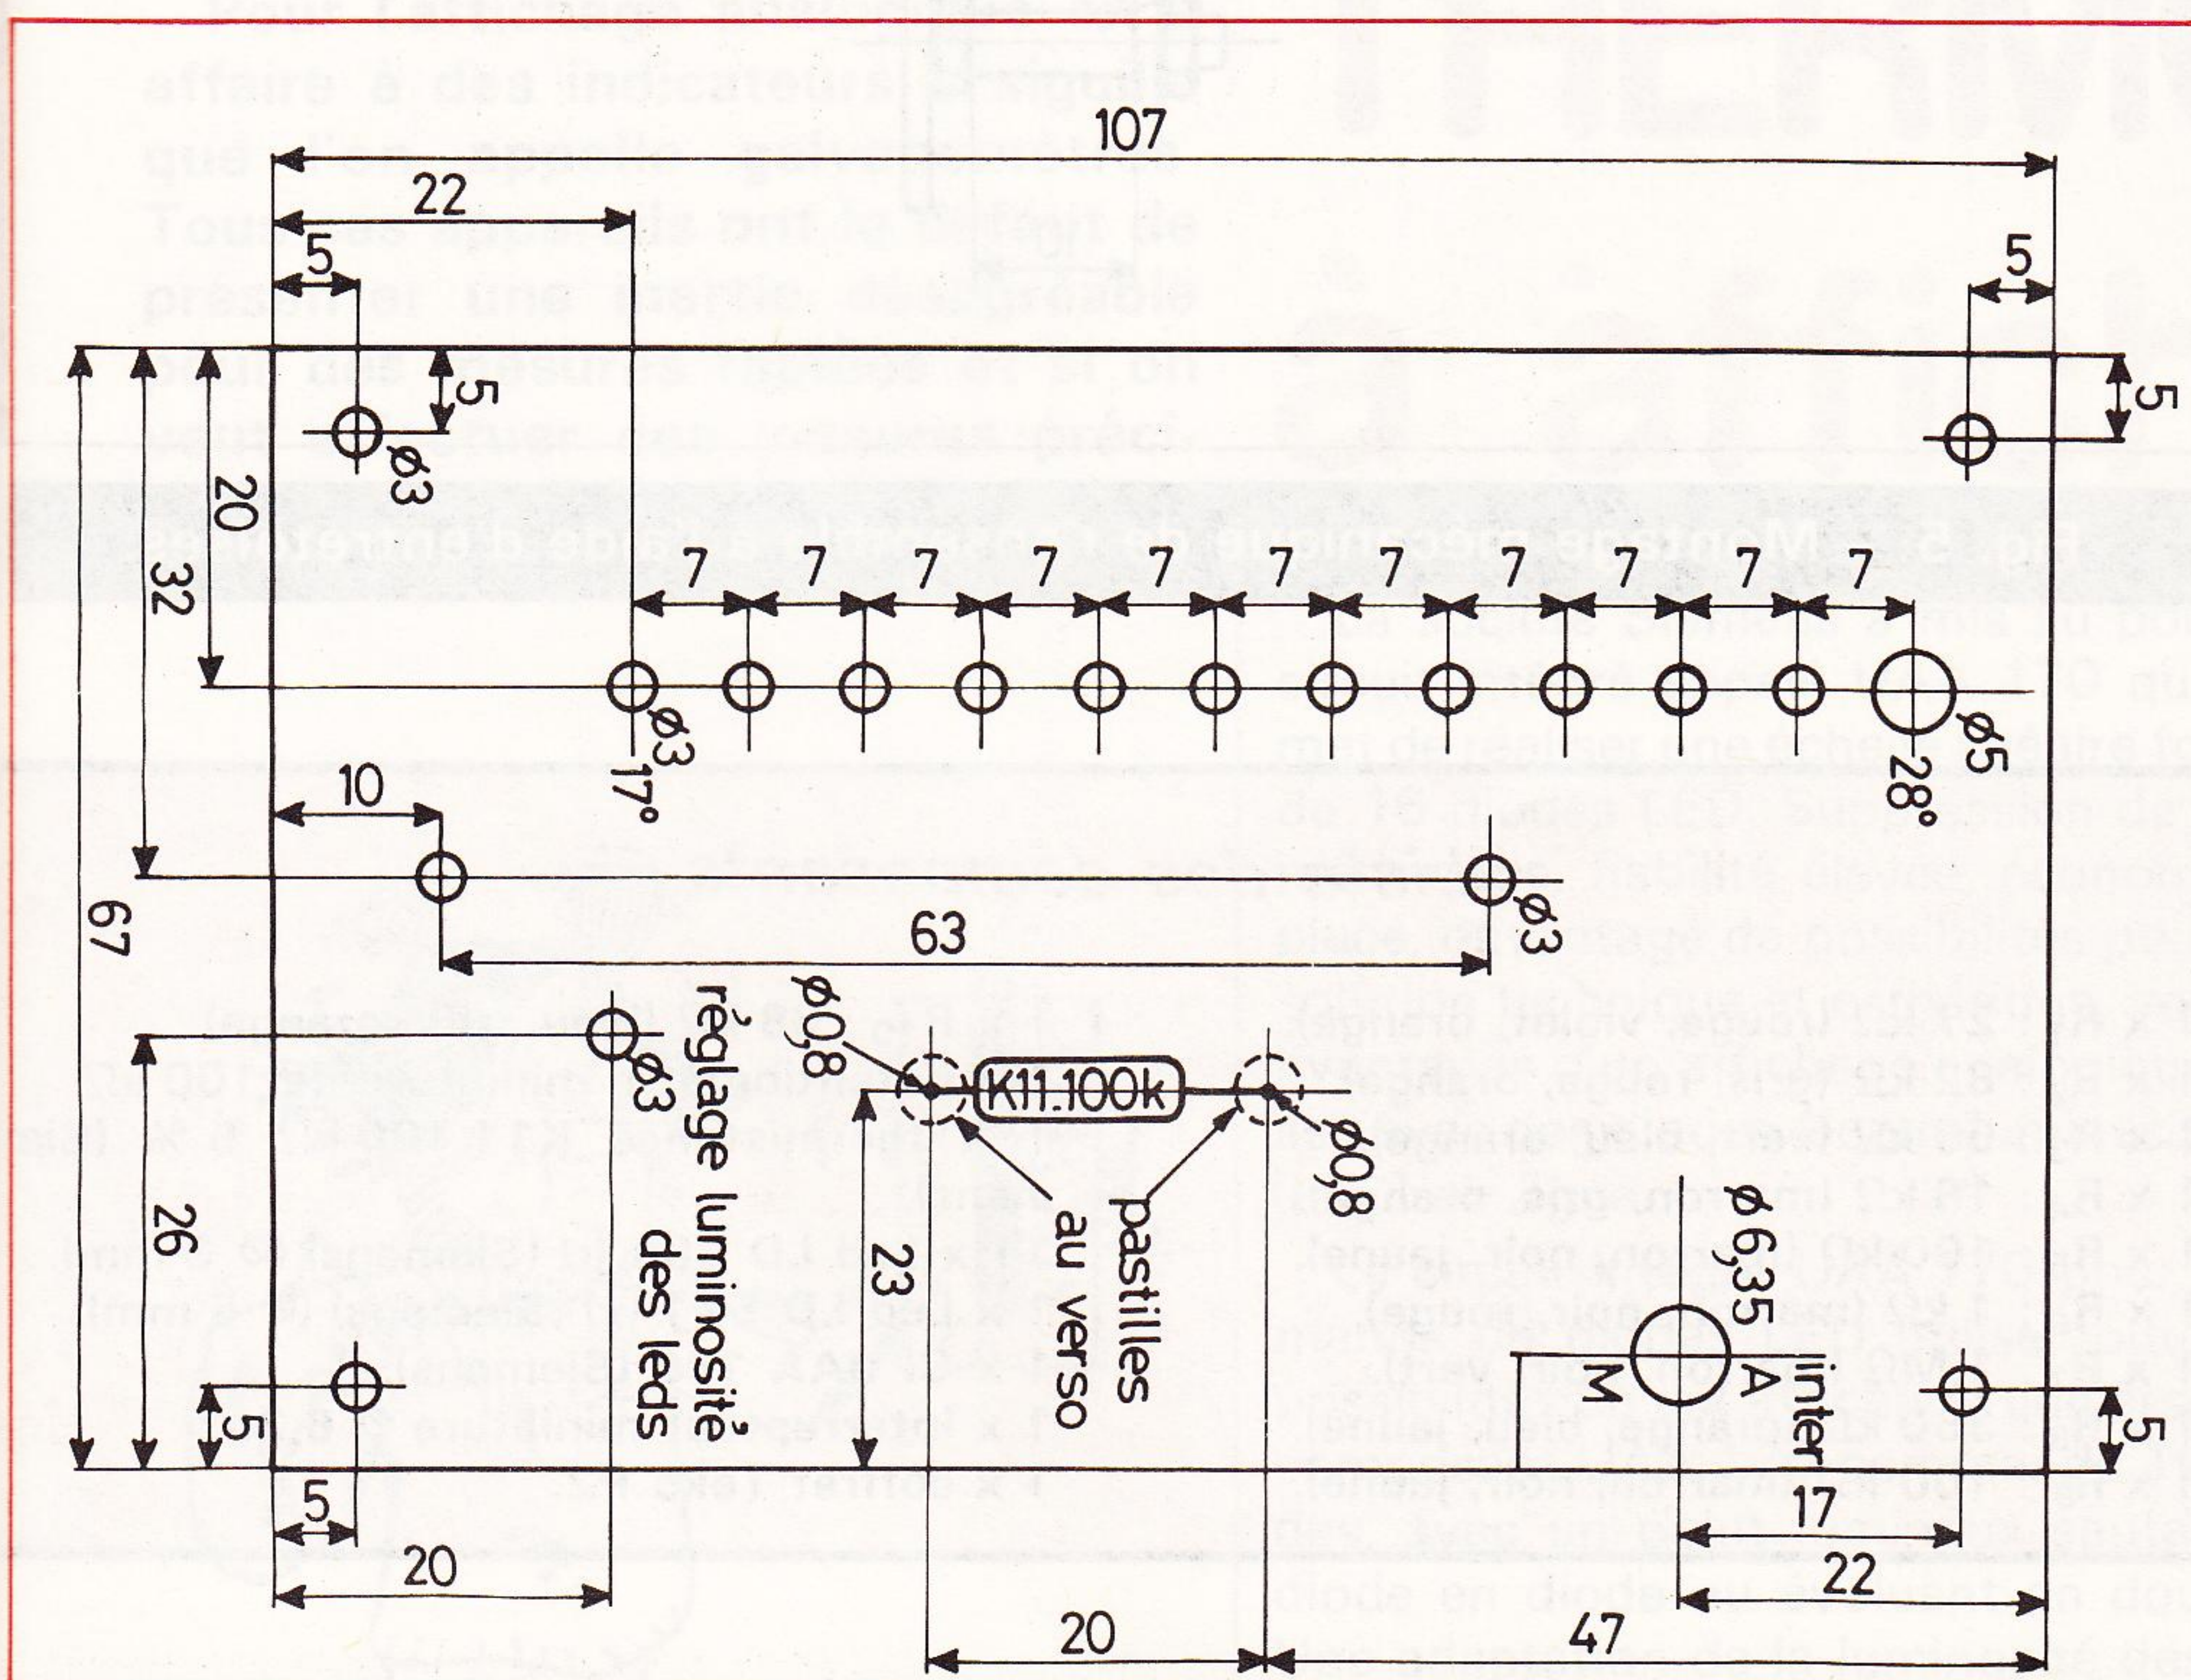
On pourra réaliser en verre époxy une plaque de la dimension d'un couvercle de boîtier P/2.
